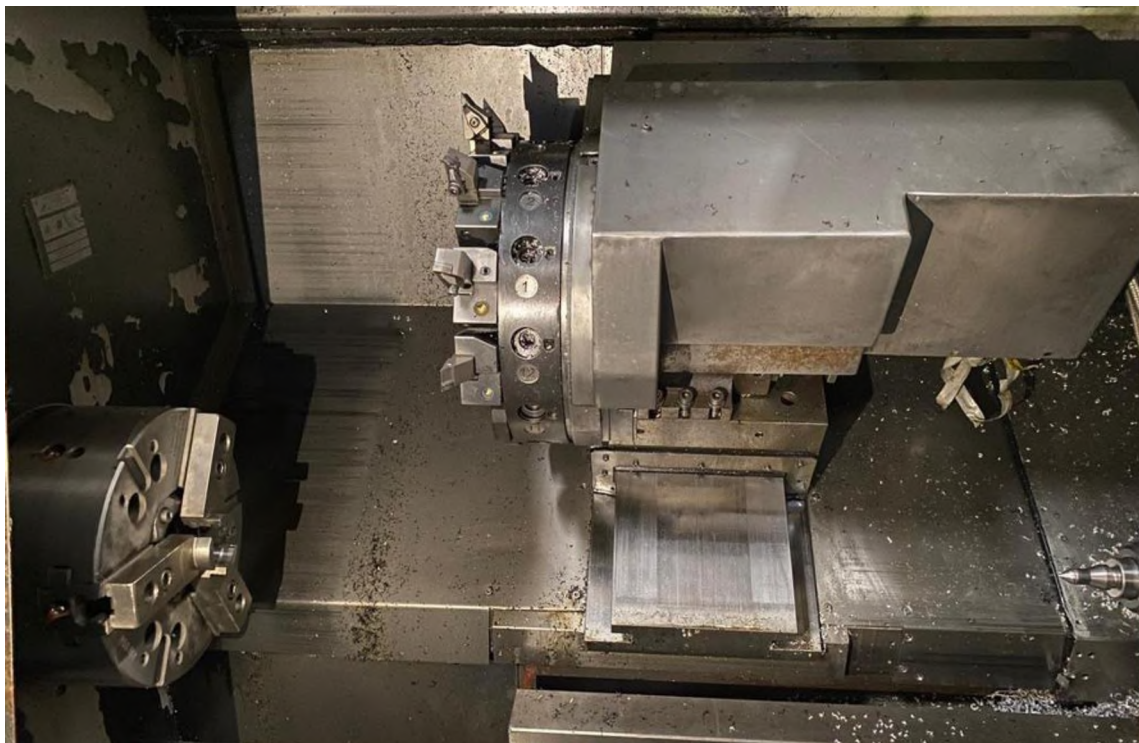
Револьверна голівка та кулачковий патрон токарного верстату Spinner TC 65 MC
